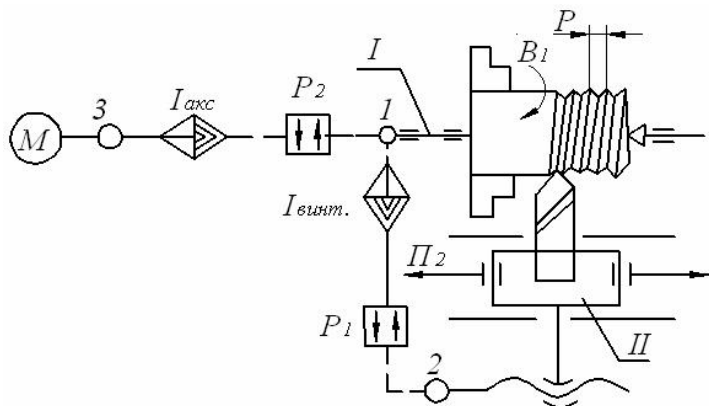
Структурная кинематическая схема токарно-винторезного станка с ручным управлением
